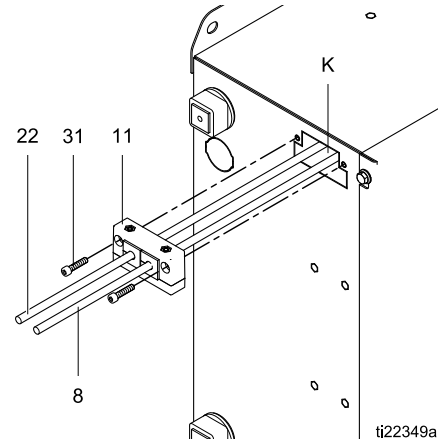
Installation der Kabeldurchführung im elektrischen Steuerkasten
